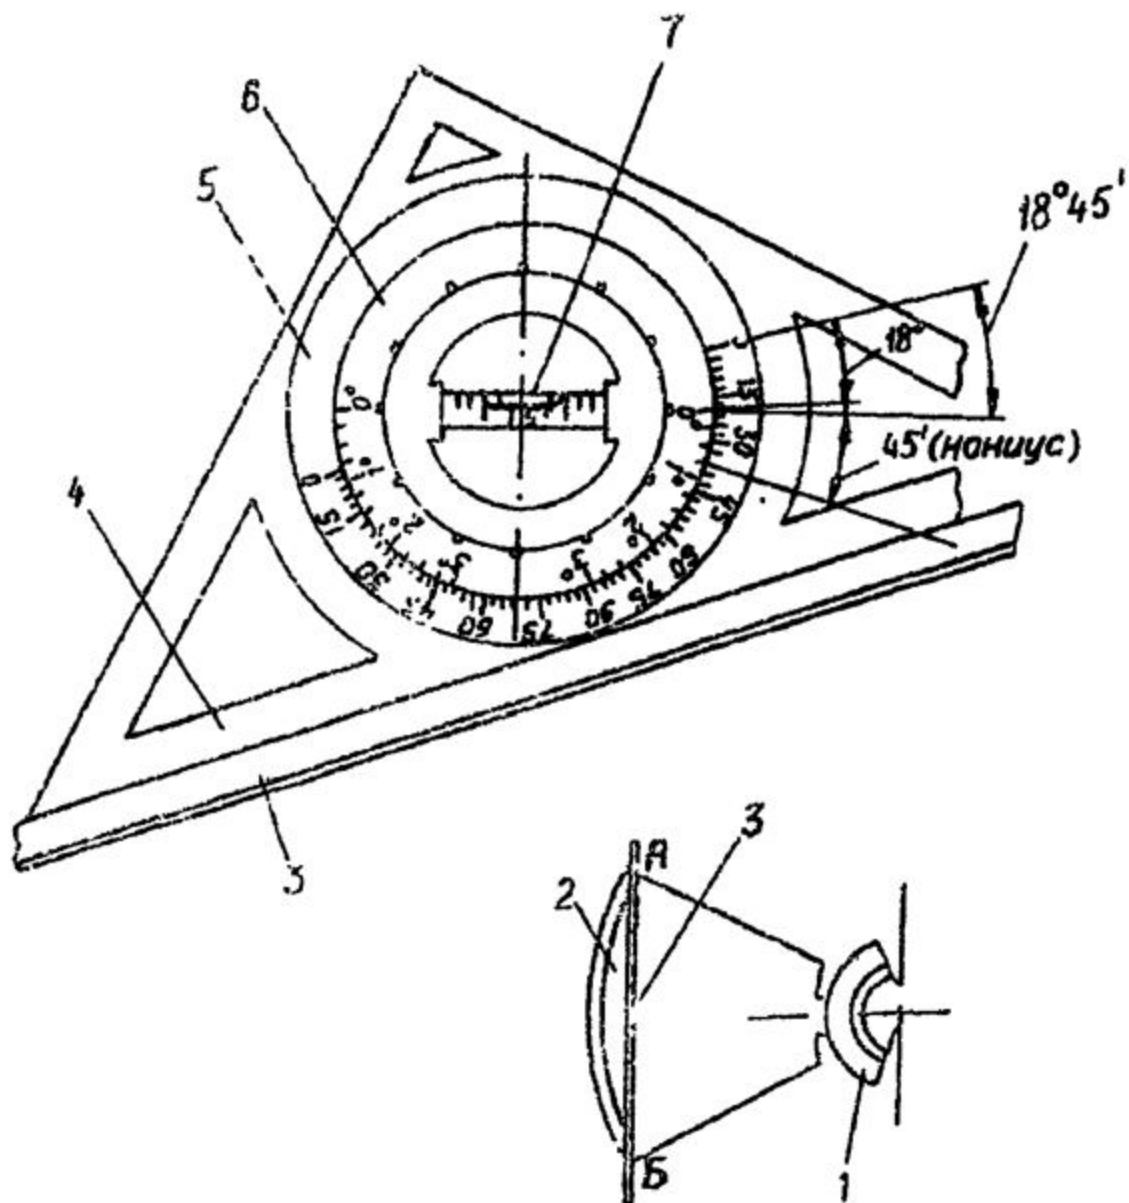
Проверка угла установки лопастей рабочего колеса угломерным устройством УУБ-VI:
